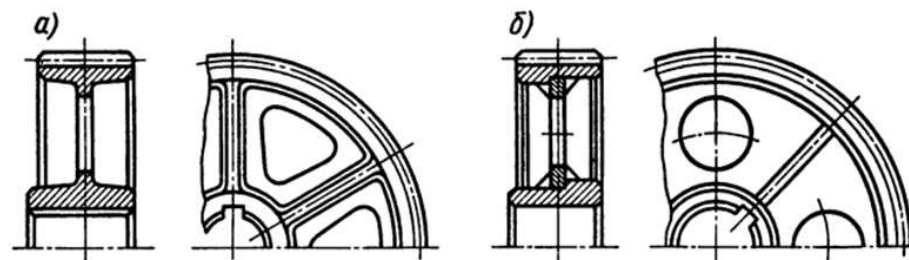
Литые (а) и сварные (б) зубчатые колеса
